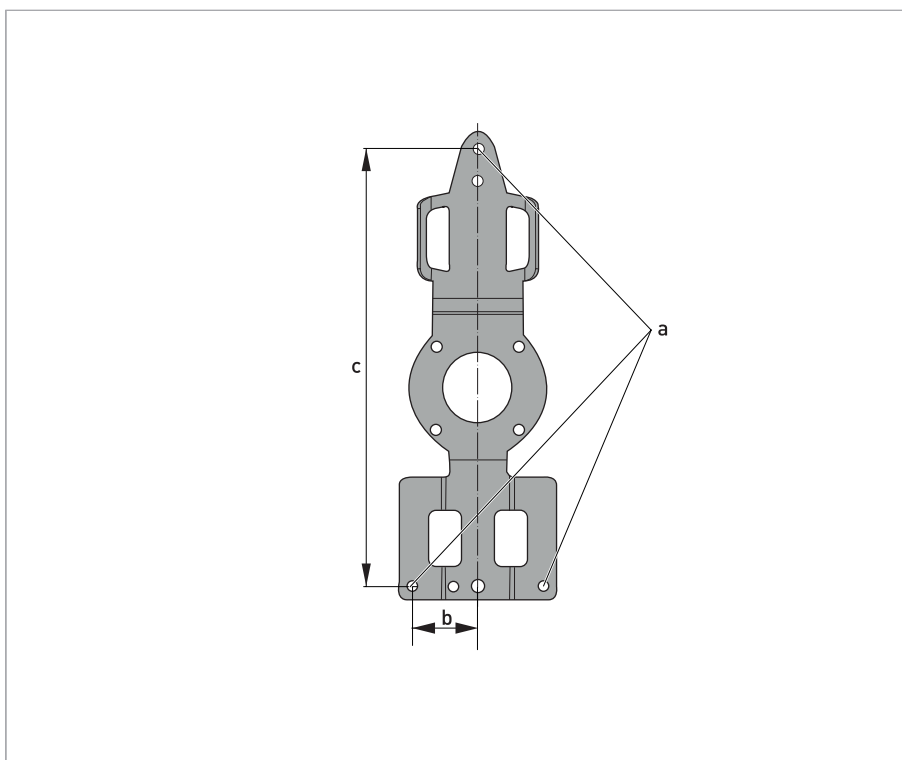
Размеры монтажной пластины корпуса для настенного монтажа из нержавеющей стали
